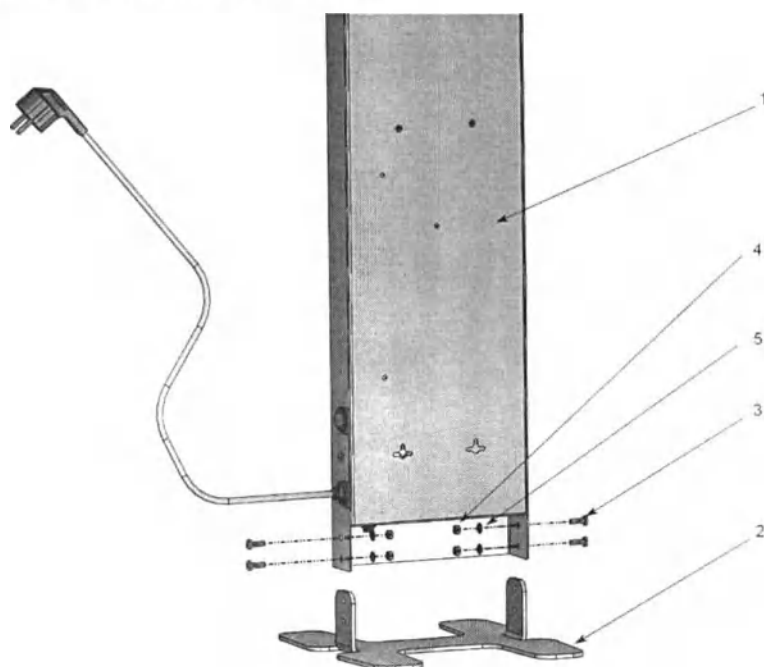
Монтаж облучателя на опорную стойку. 1- Облучатель; 2- Опорная стойка; 3- Винт М5; 4- Гайка М5; 5 – Шайба 5.
